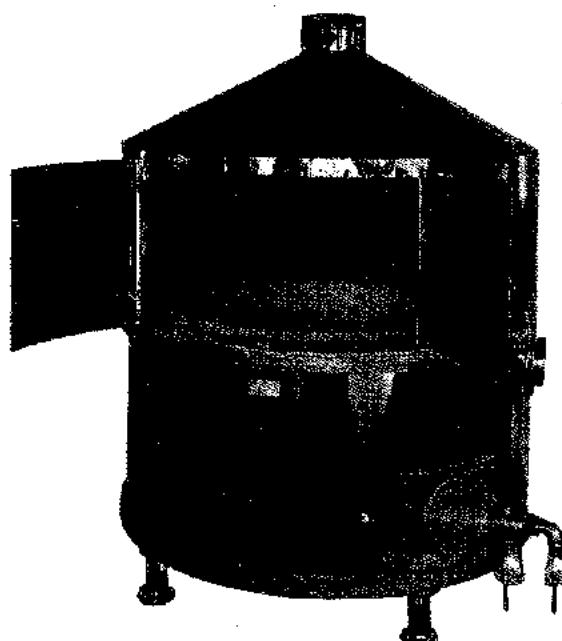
Cuba de plomo (Bellevue Industrial Furnace Co.)
